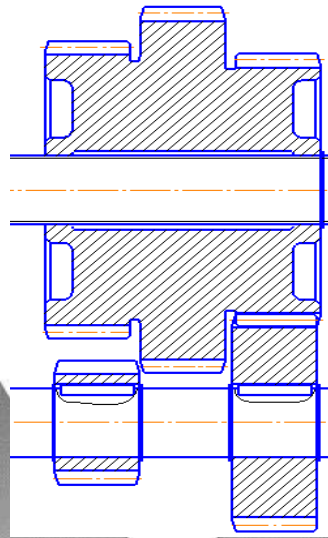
Конструктивна схема переміщення та положення блока зубчастих коліс Б2– зачеплення Z40/Z40.
